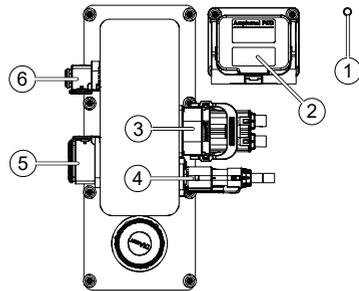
Batteria ad alta tensione – Panoramica di connettori e collegamenti
